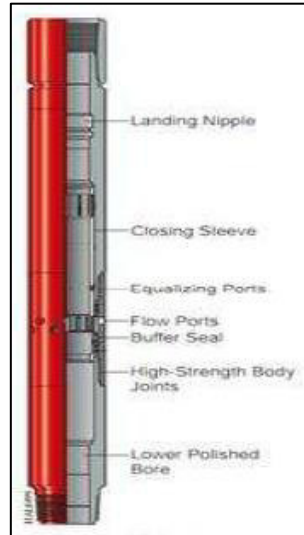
SLEEVE SLIDING SIDE DOOR
